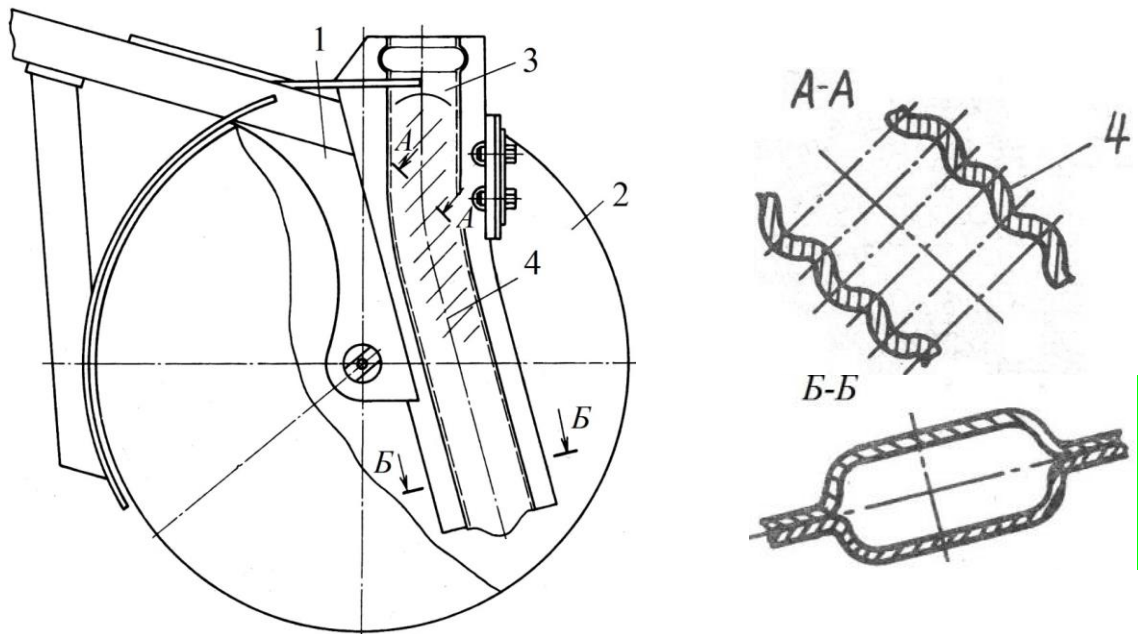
Сошник: 1 – корпус; 2 – диск; 3 – направляюча лійка; 4 – гофри
